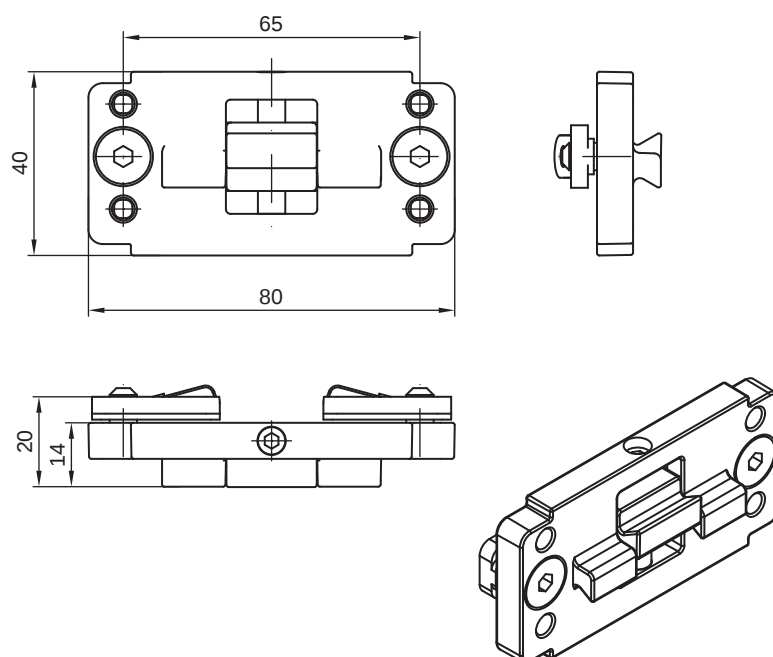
Supporto di serraggio BT-P40 per il fissaggio nelle colonne di fissaggio UDC
